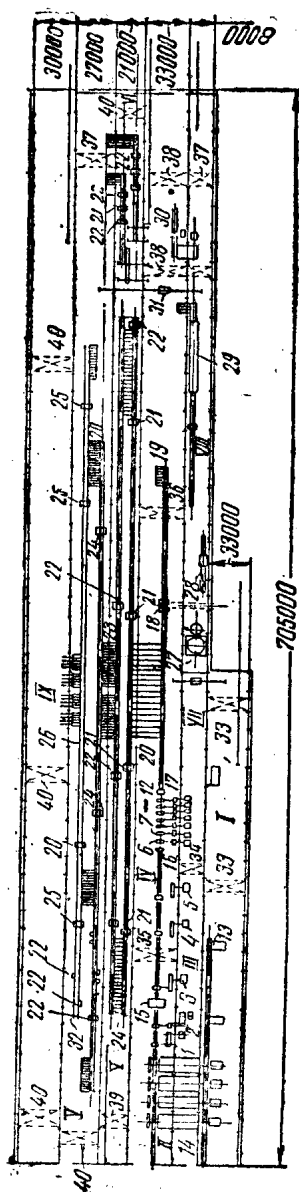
2500公厘連續式鋼板軋軋机的設備布置平面图
